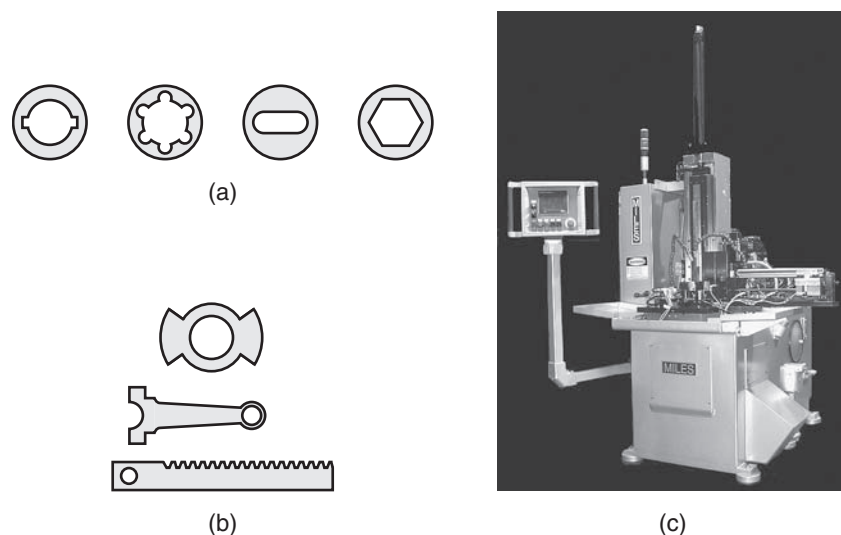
(a) Partes comunes producidas mediante brochado interno. (b) Partes fabricadas mediante brochado de la superficie. (c) Máquina de brochado vertical. Fuente: (a) y (b) Cortesía de General Broach and Engineering Company; (c) Cortesía de Ty Miles, Inc.
